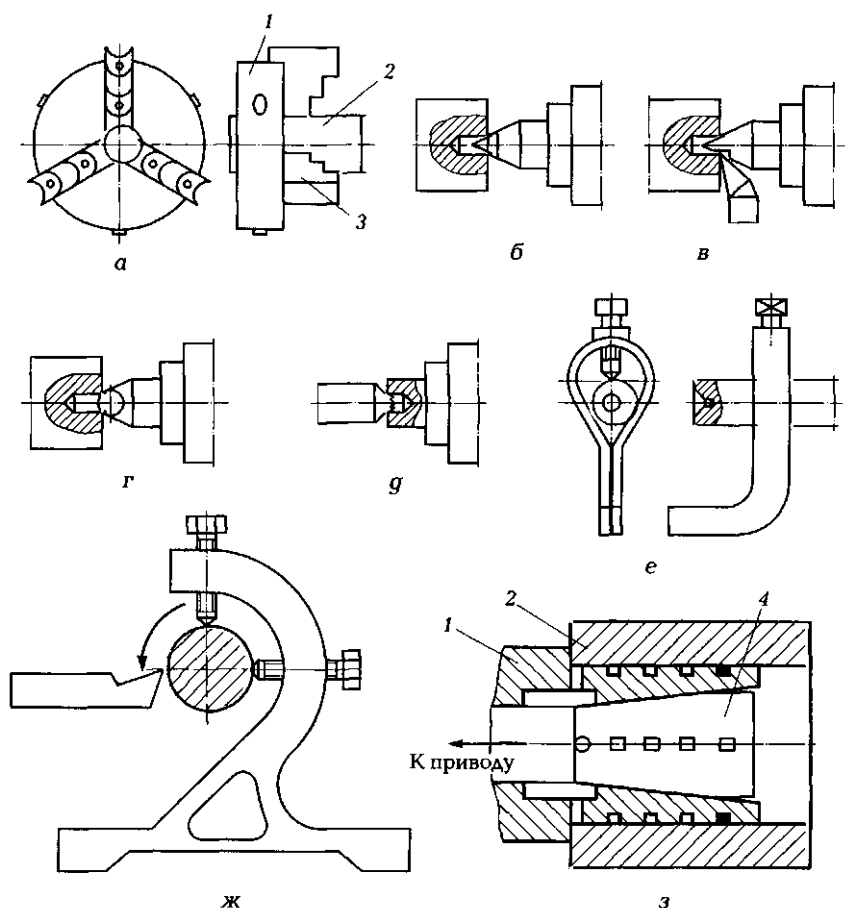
Рабочие приспособления, применяемые в токарных станках:
